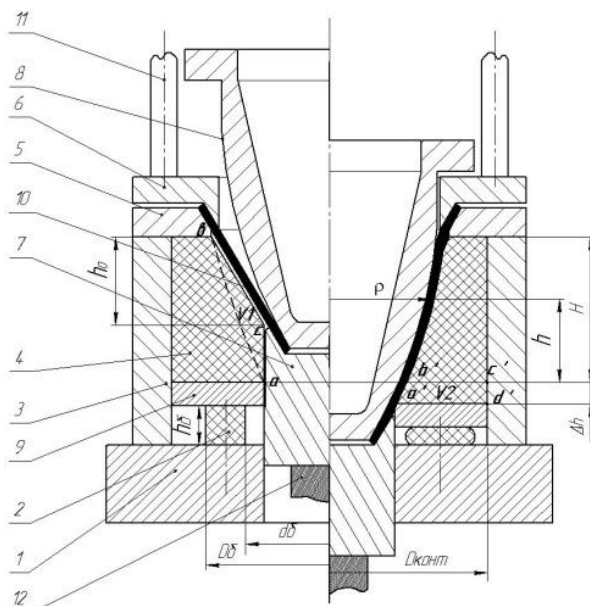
Схема устройства для формообразования выпуклых тонкостенных деталей
